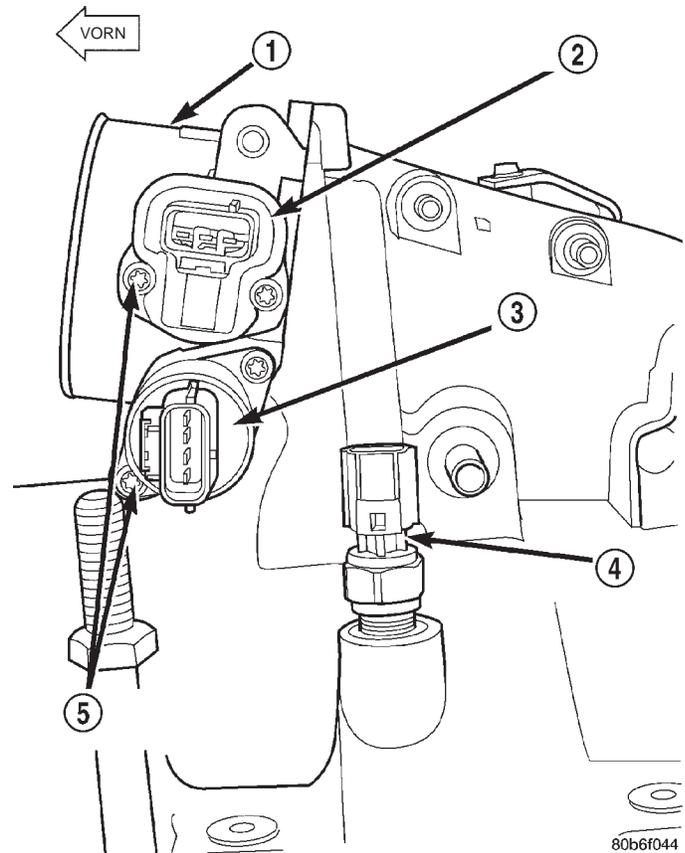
TPS-Befestigungsschrauben—4.7L-V8-Motor
